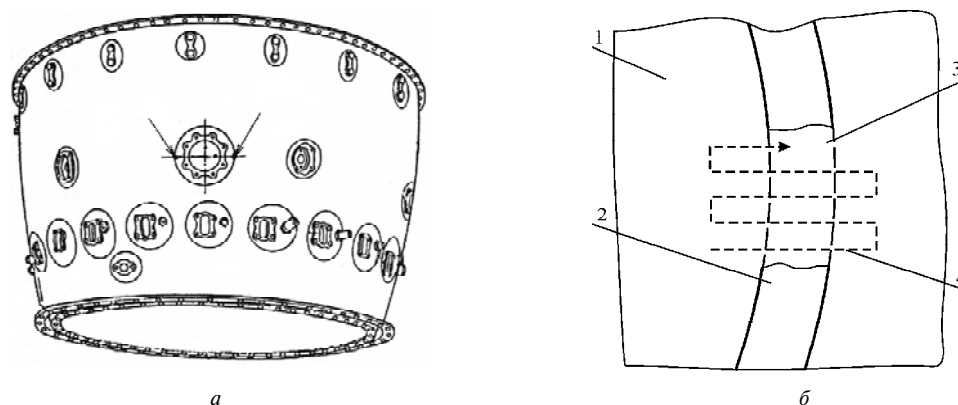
Наружний корпус камери сгорання (а) и схема контроля опасных участков сварных соединений (б):
